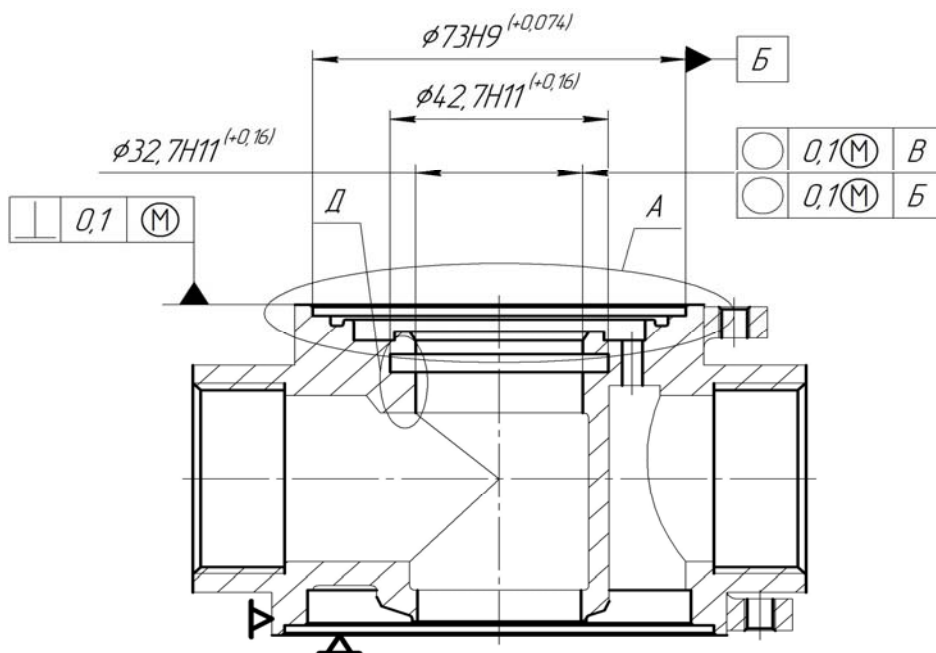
Эскиз корпуса с канавками, изготовленного на станке Daewoo Lynx 210A
